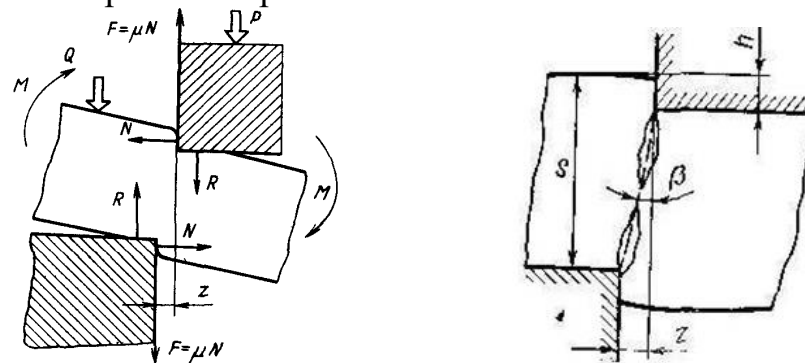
схема действия сил положения (а) и положения скалывающей трещины (б) при отрезке.
